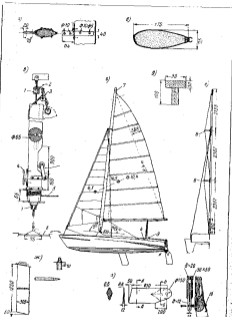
План корпусности и детали обшивки, рули и швертового устройства: а — крепежные отверстия на мачте; б — сечение мачты; в — штаг; г — план корпусности; д — сечение палубы; е — прокладка штага; ж — шверт; з — руль.
